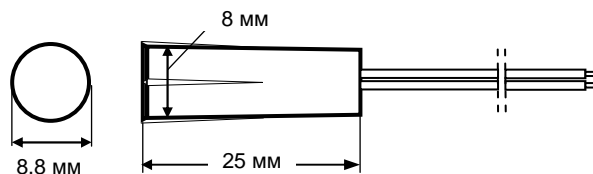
Геркон извещателя К-2 в пластмассовом корпусе
